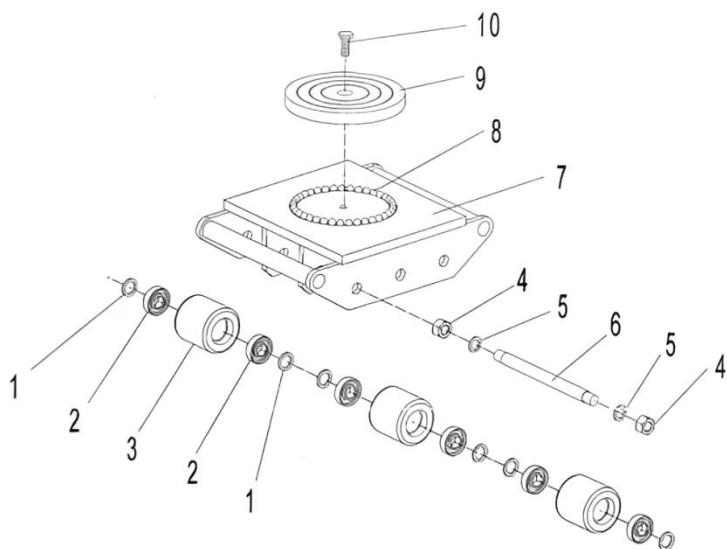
Взрыв-схема роликовой платформы CRA 9.
